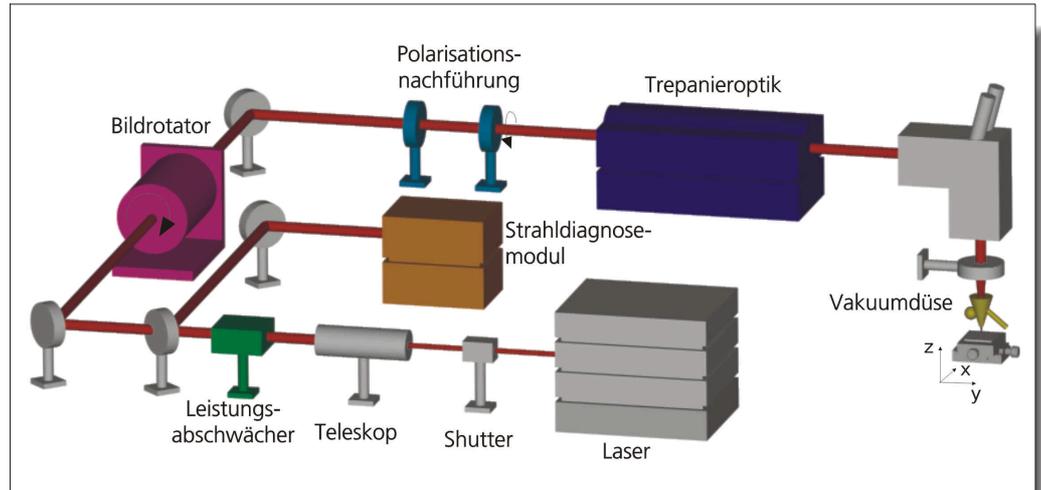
Systemtechnik für die Erzeugung präziser Bohrungen unterschiedlichster Geometrien.
